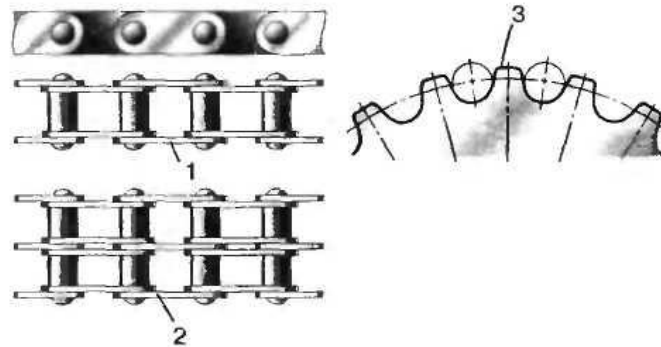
Візуалізація зубчастого сектора зірочки та частини ланцюга для розуміння точок передачі зусилля при обертанні: 1 – загальний вигляд однорядного ланцюга; 2 – загальний вигляд дворядного ланцюга; 3 – зубці та западини, що відповідають профілю ланцюга, що використовується.
